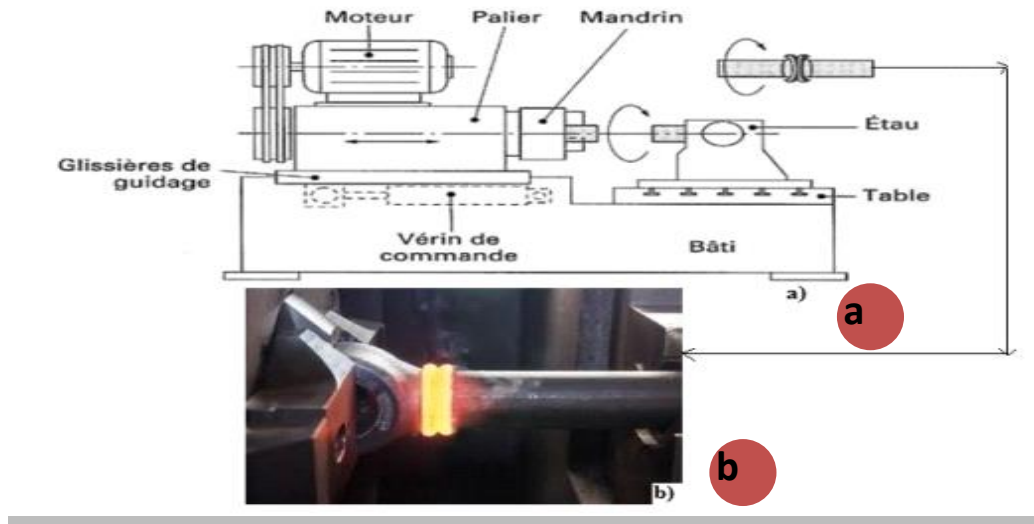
Soudage par friction ; (a) Schéma d'une machine de soudage par friction, (b) Exemple de soudage pour la fabrication des vérins hydraulique [2].
